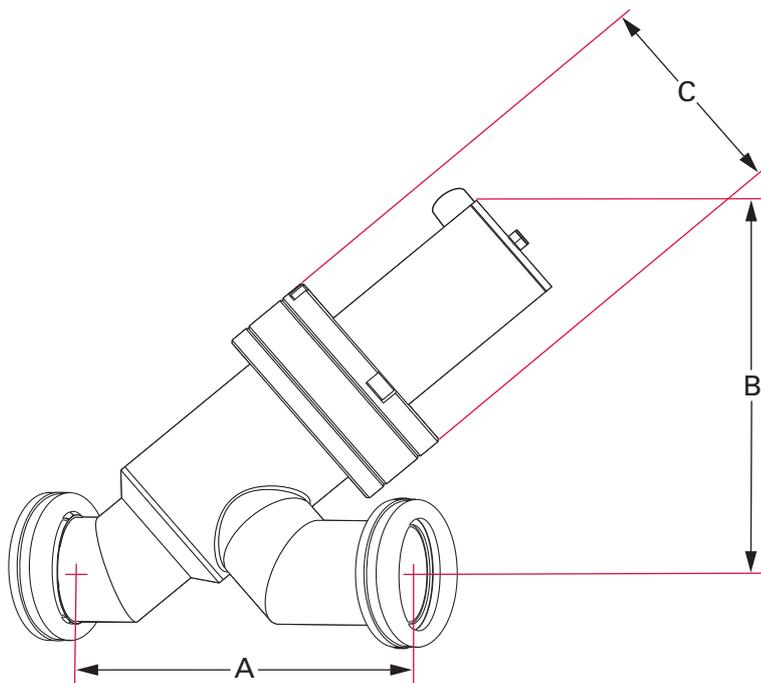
Abmessungen der pneumatischen Inline-Ventile
